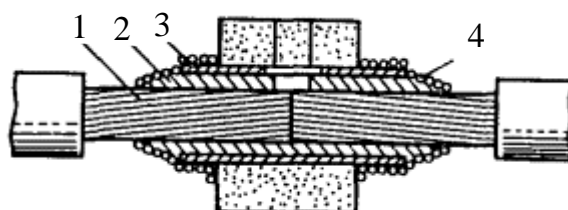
Подготовка алюминиевых жил кабелей 20 и 35 кВ сечением 25-185 мм² к термитной сварке
